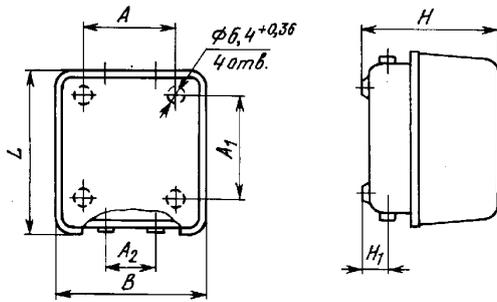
Габаритные, установочные размеры пускателей реверсивных типов ПМ12-080, ПМ12-100, ПМ12-160 степени защиты IP40
